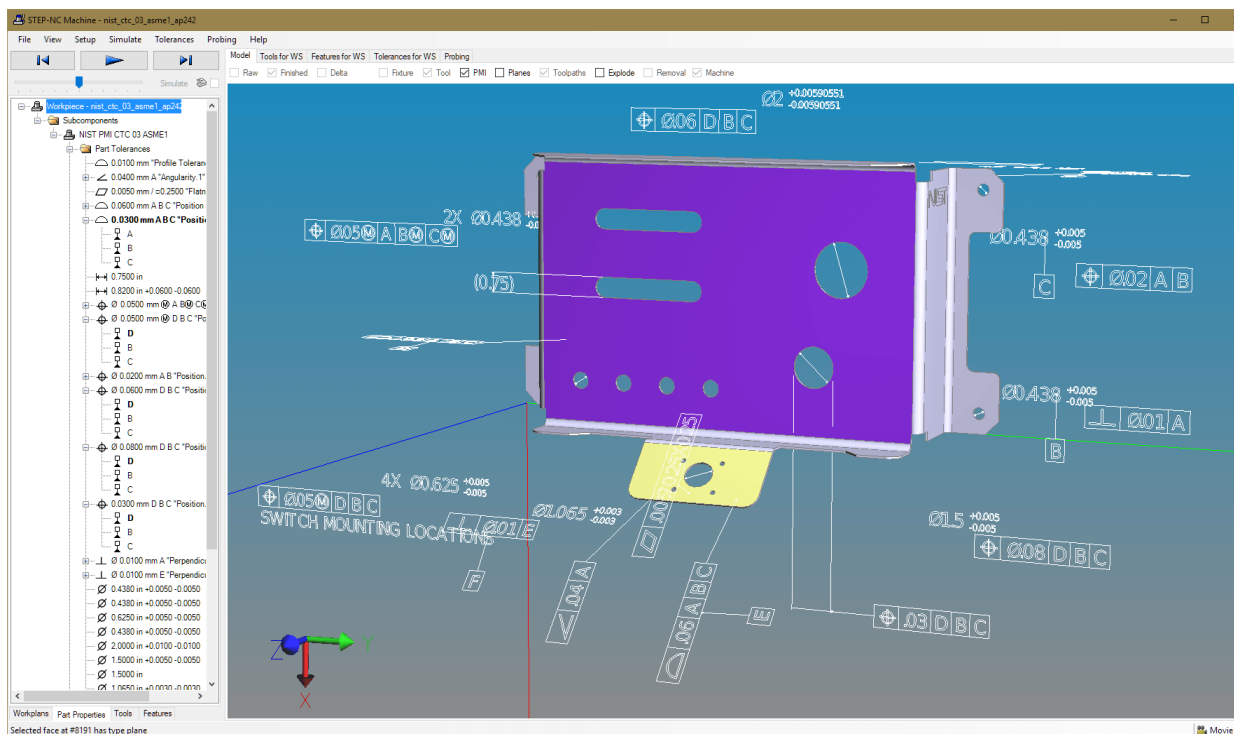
Применение файла STEP-NC для обработки деталей: текстовый файл (слева); допуски для обработки (справа)
